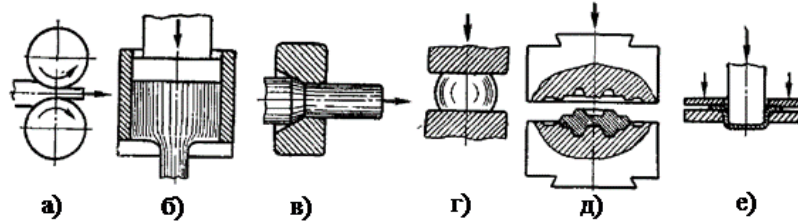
Схеми основних видів обробки металів тиском: а – прокатування; б – пресування; в – волочіння; г – кування; д - об'ємне штампування; е – листове штампування.
